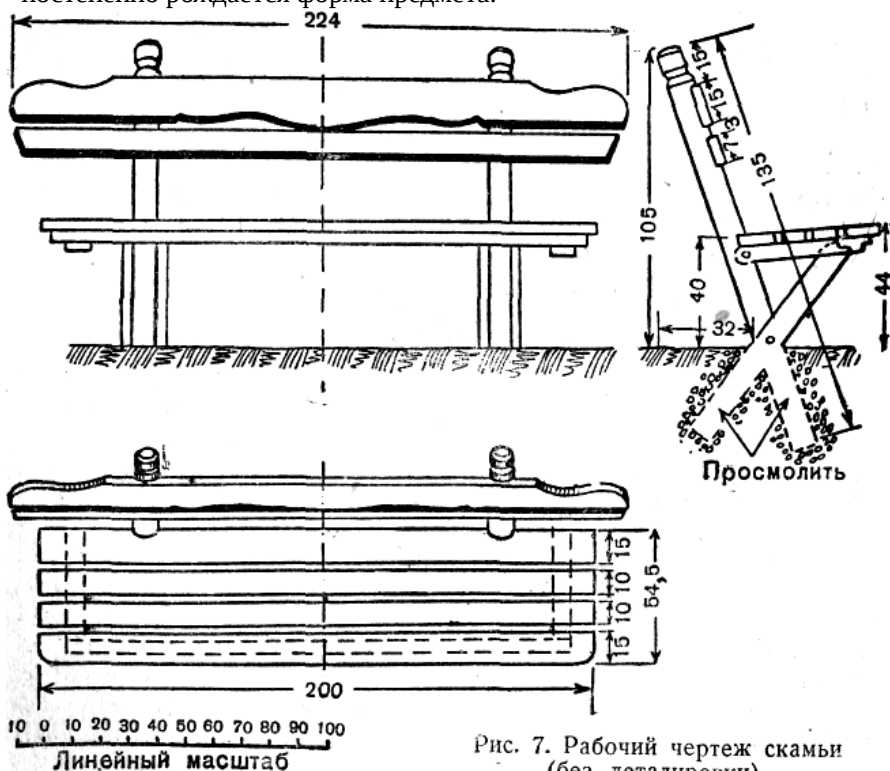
Рабочий чертеж скамьи (без детализовки).
